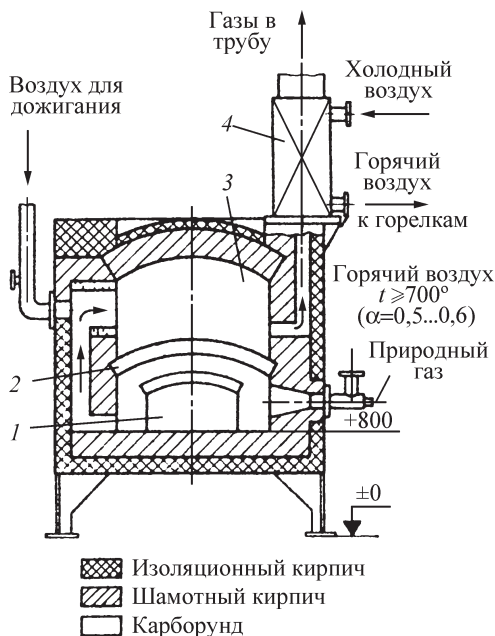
Малая рекуперативная печь для безокислительного нагрева заготовок открытым пламенем: 1 — нижняя рабочая камера; 2 — карборундовый свод; 3 — камера дожигания; 4 — жароупорный рекуператор
